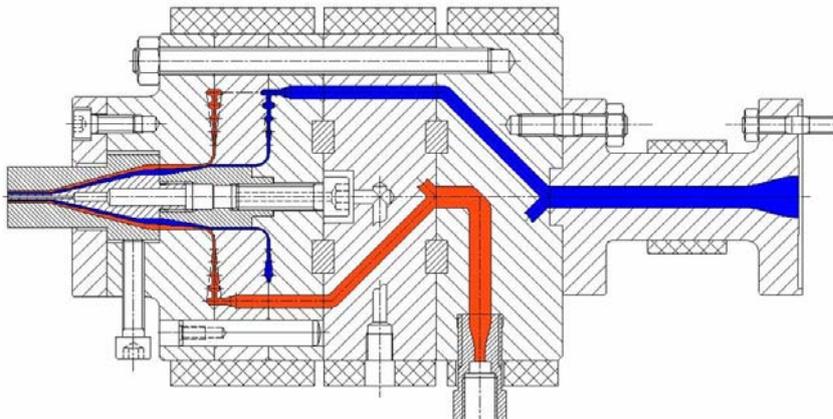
Coextrusionswerkzeug mit Spiral-Wendelverteiler
